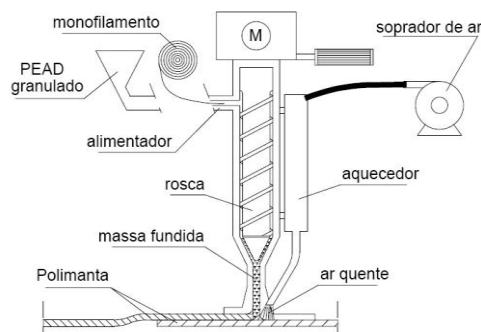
Representação esquemática de uma soldadura por extrusão.
